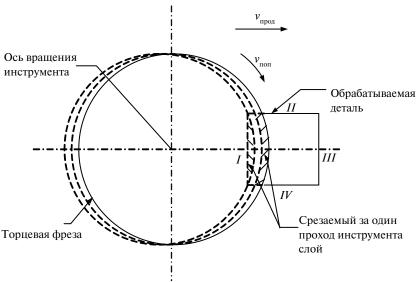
Кинематика перемещения фрезы в процессе обработки полимерного образца: I—IV — серии экспериментов.
